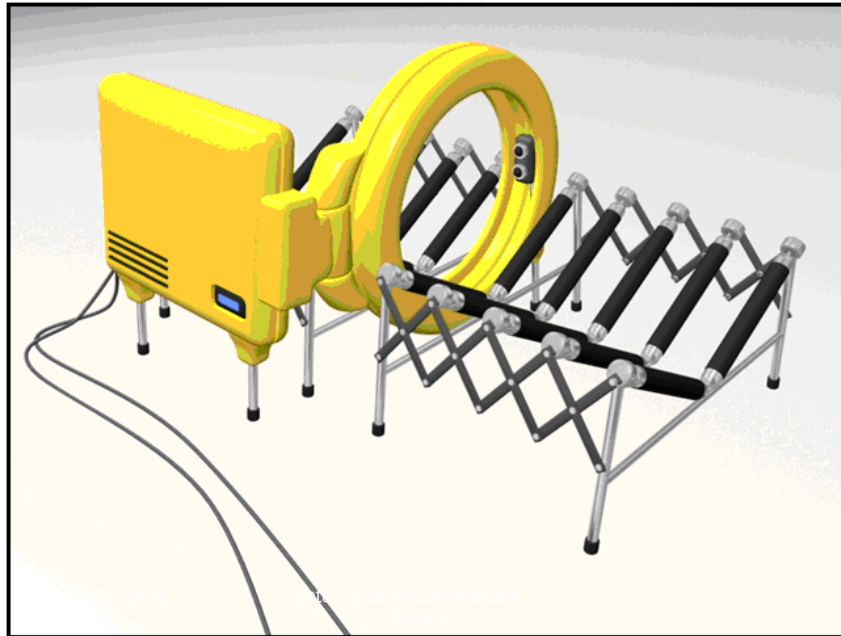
Vista exterior del sistema de reconstrucción de volúmenes [18]
